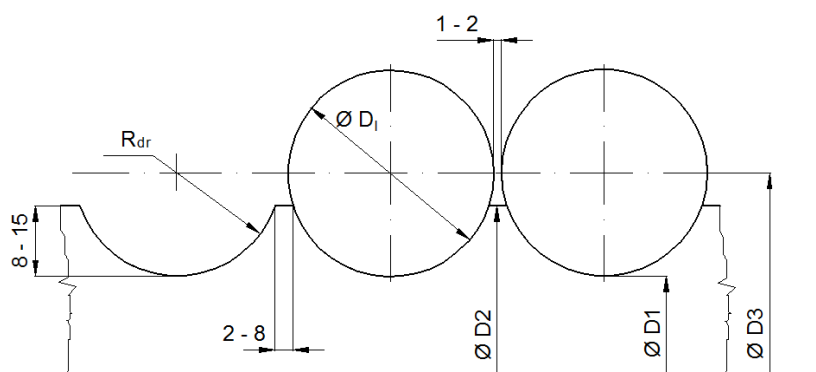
Jedna z frézek užívaných pro obrábění deskového obložení bubnů těžních strojů.
